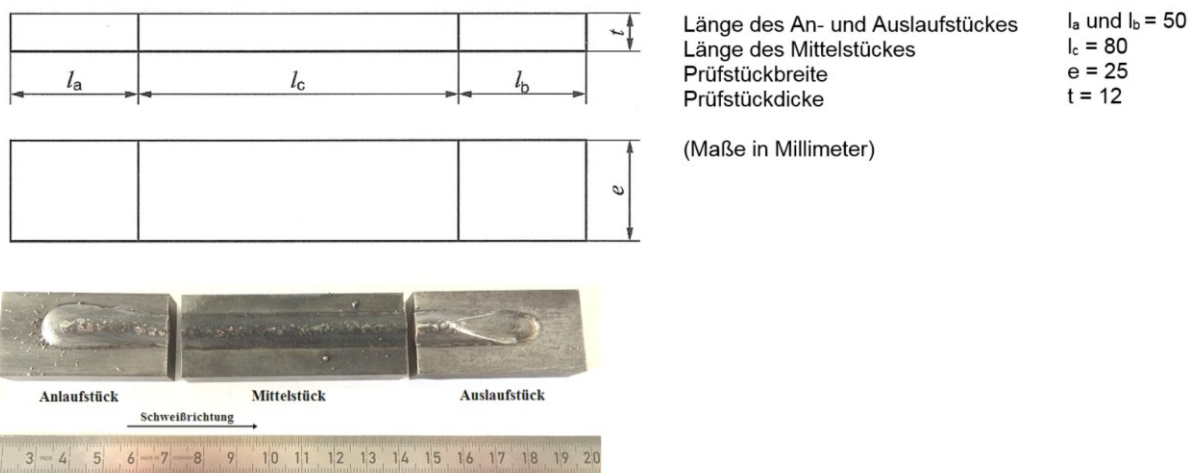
Verwendete Probengeometrie nach DIN EN ISO 3690 (Prüfstücksatz A) und exemplarisch geschweißte Probe
